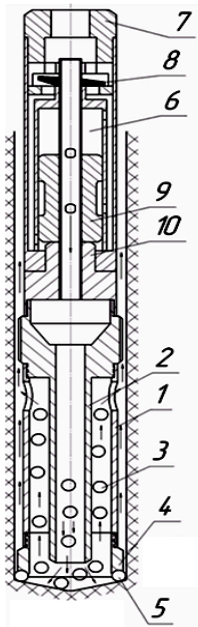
Загальна схема пневмомеханічного пристрою для буріння свердловин
